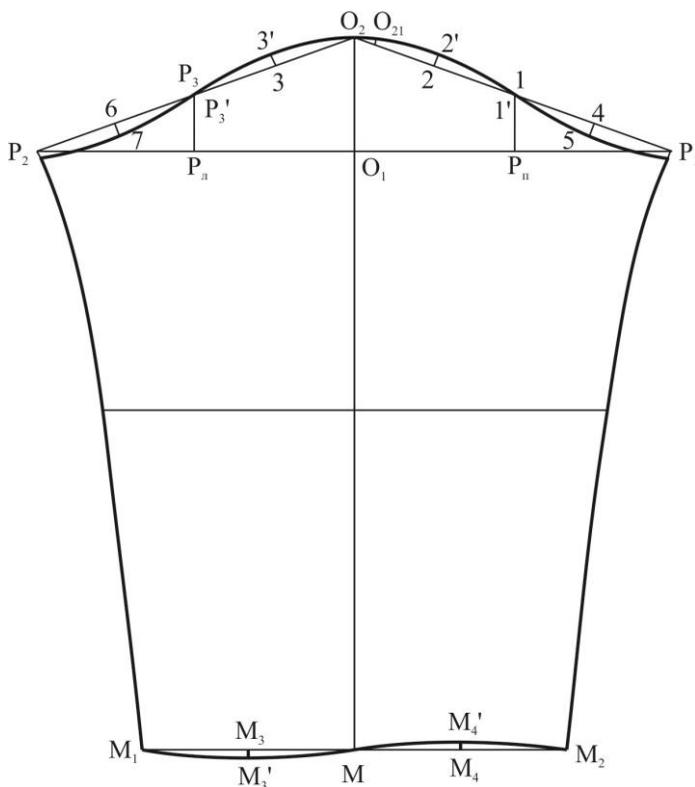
Чертеж конструкции мужских изделий с рукавами рубашечного покрова с овальной проймой
